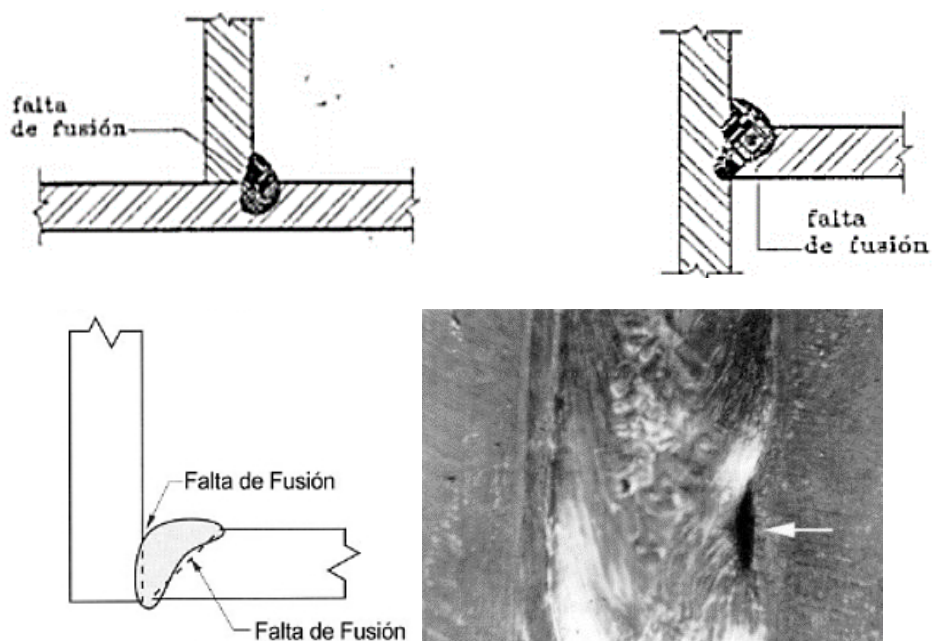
Detalle de falla en conexión soldada por falta de fusión
